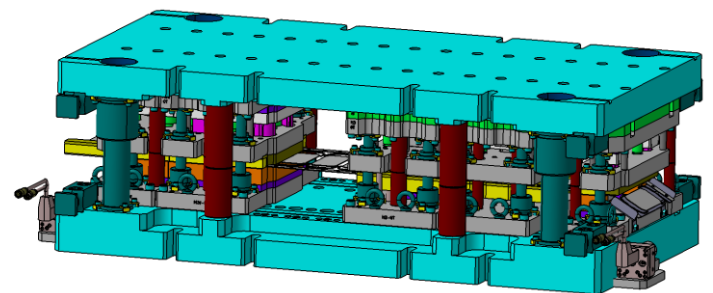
Demonstrator Folgeverbundwerkzeug
